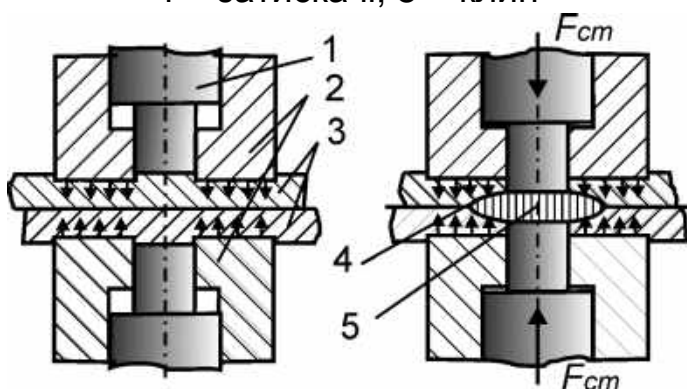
Схема зварювання з попереднім стисненням: 1 – пуансон; 2 – притискач; 3 – зварювані деталі; 4 – периферійна зона зварювання; 5 – внутрішня зона зварювання
